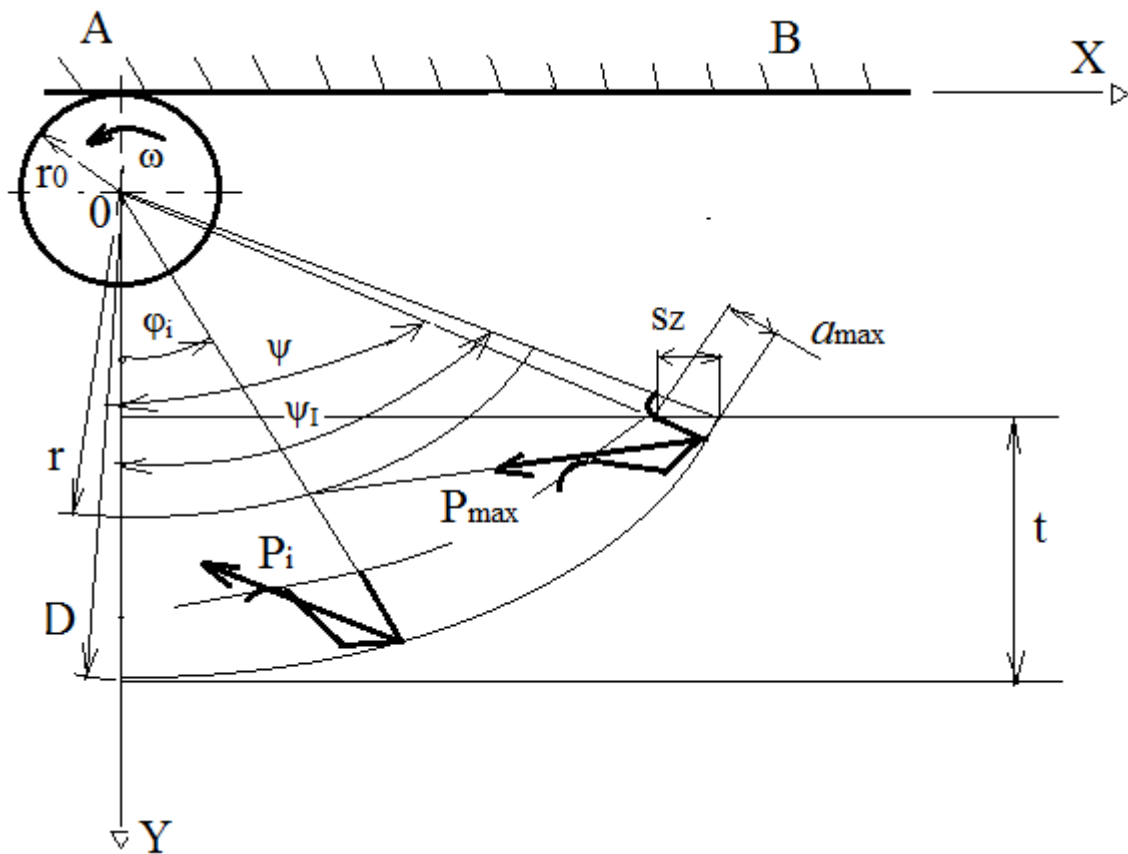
Розрахункова схема зусиль при зустрічному фрезеруванні
